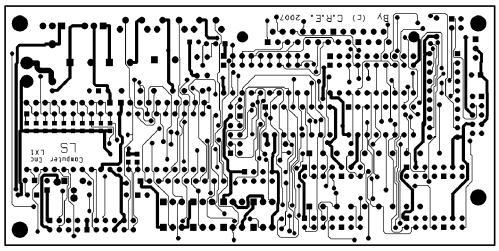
il master e il piano di montaggio dei componenti del driver dei motori.
